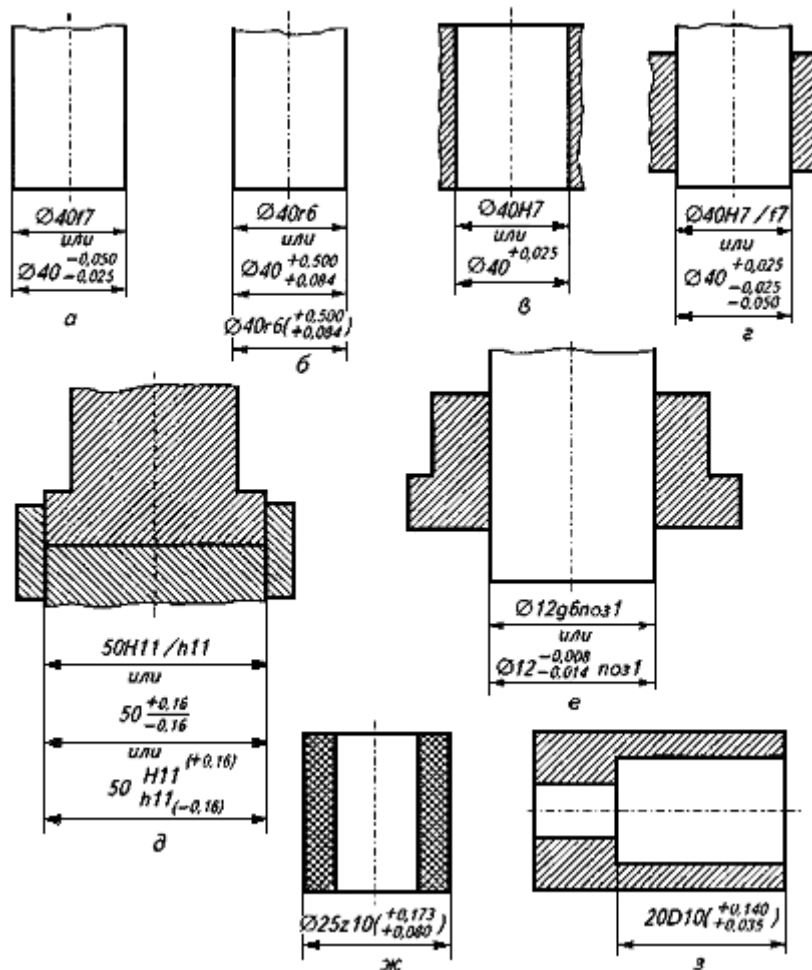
Примеры обозначения полей допусков и посадок на чертежах
